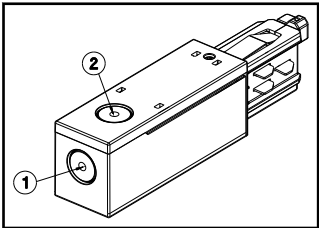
Pareti sfondabili della testata - Pic.2 Knock-out walls
